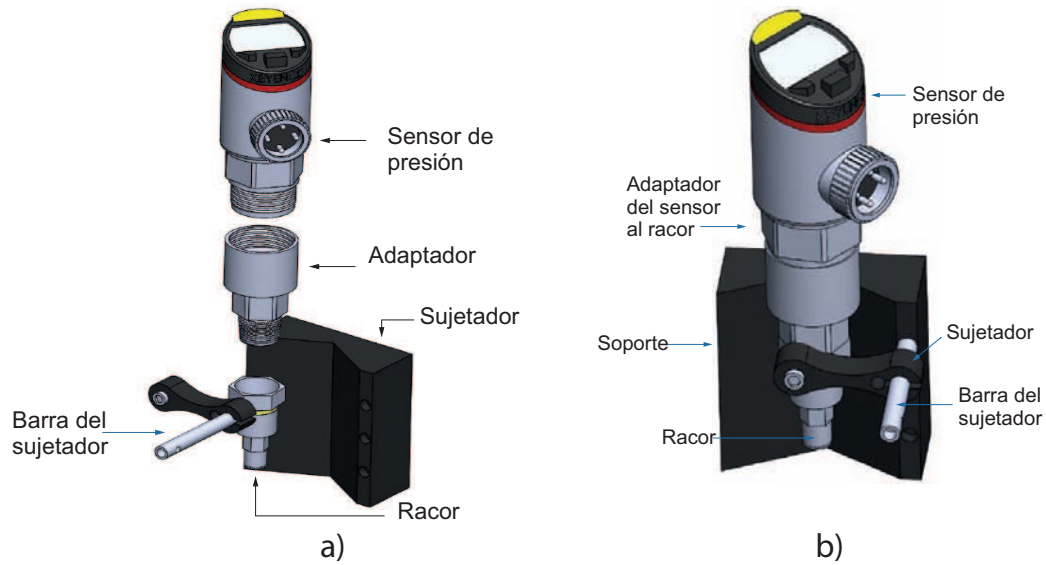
Sensor de presión y sus elementos de montaje y conexión. a) Esquema en explosión del sensor de presión, b) Ensamble de elementos de sujeción y conexión del sensor de presión para montarlo en la cámara de presión.
